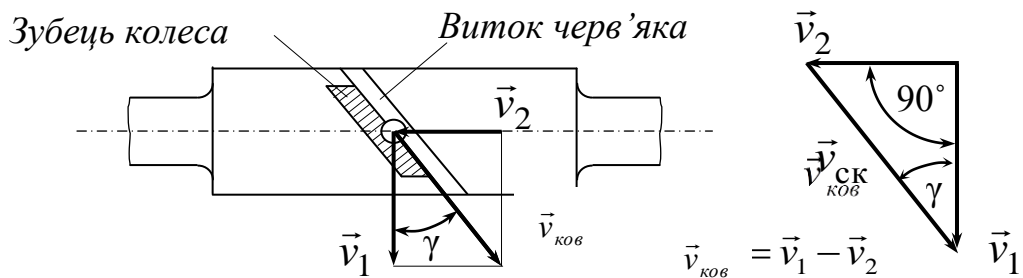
Зв'язок швидкостей в черв'ячній передачі
